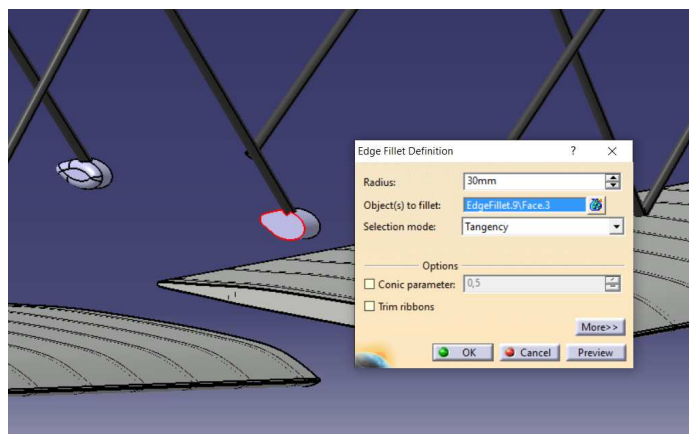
Edge Fillet* aplicado a la unión metálica de barras con fuselaje
